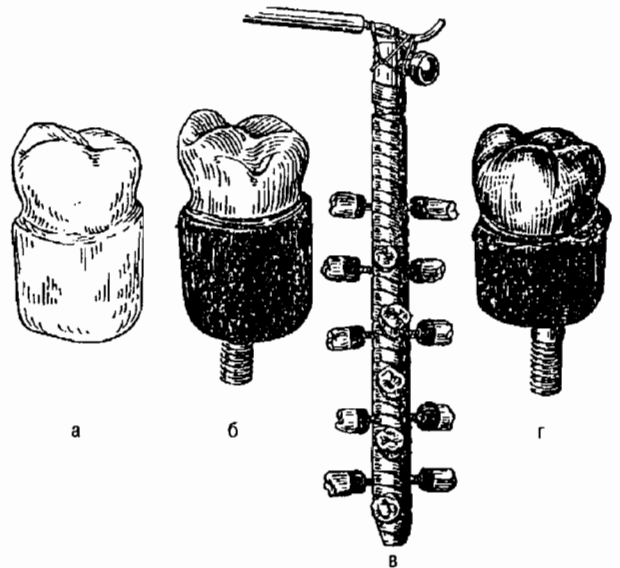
Процесс изготовления коронки и кап гальваническим путем: а — заготовка гипсовой модели коронки зуба; б — нерабочая часть модели изолирована лаком; в — модели коронок зубов укреплены на подвески для погружения в ванну; г — металлическая коронка после отложения металла.
